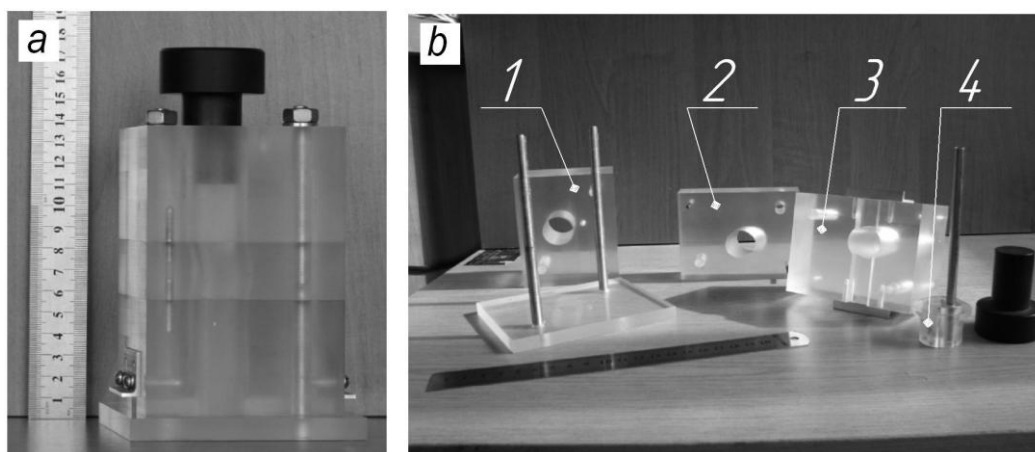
Фотография плексигласовой матрицы для винтовой экструзии пластилиновых заготовок круглого сечения
